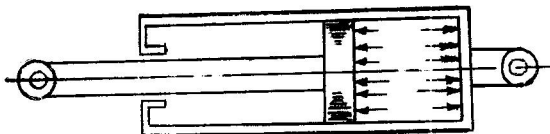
Пневматичний зрівноважувальний механізм
